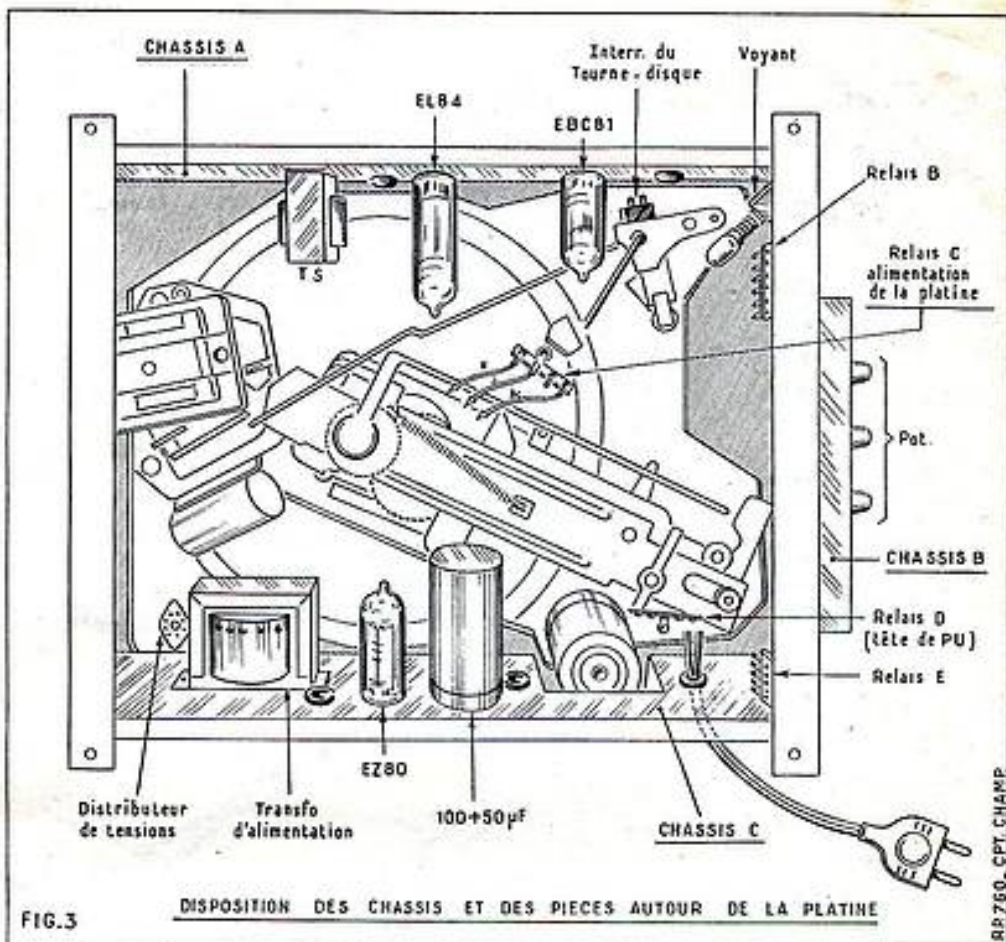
DISPOSITION DES CHASSIS ET DES PIÈCES AUTOUR DE LA PLATINE
